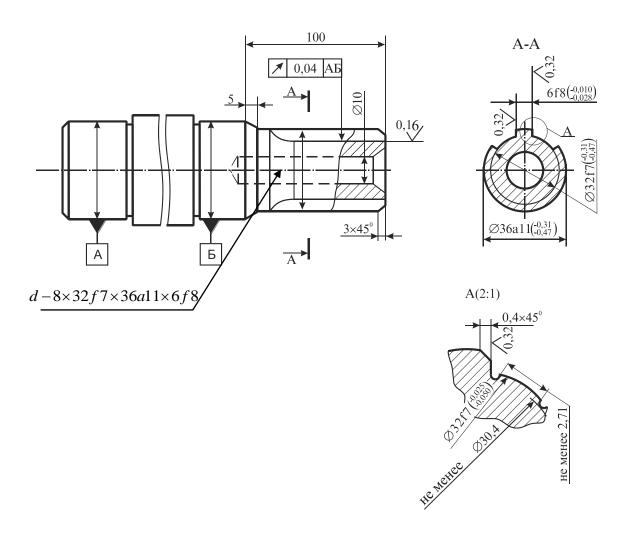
Пример оформления рабочего чертежа шлицевого вала
